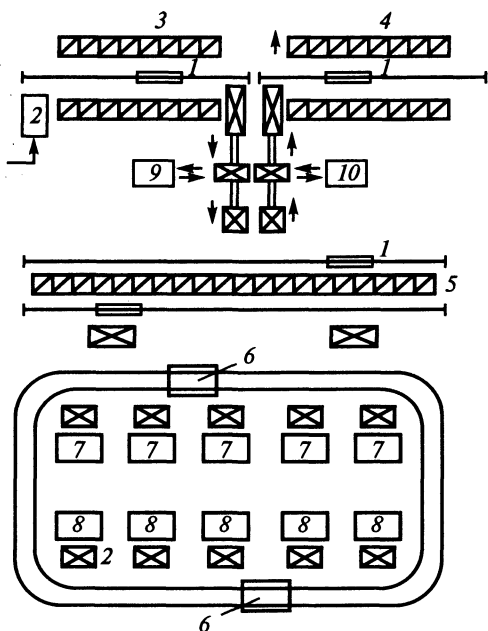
Компонновка гибкой системы для обработки корпусных деталей (мелкосерийное производство):
